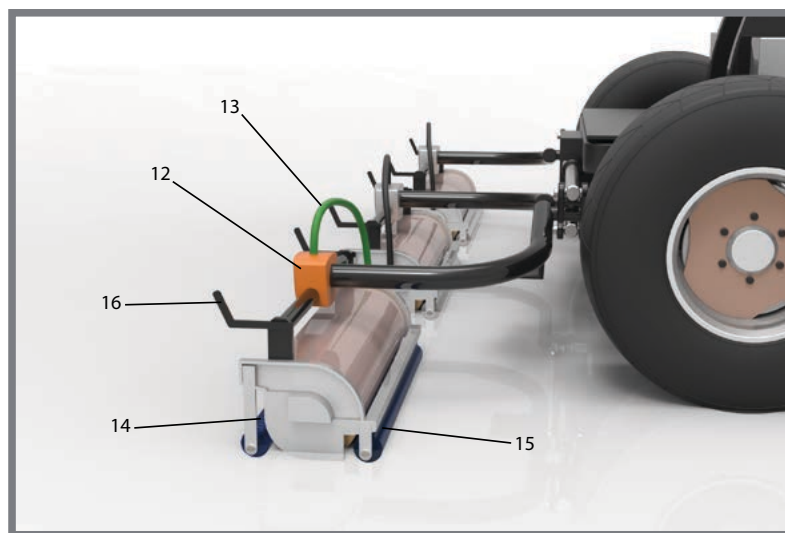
Finální technické řešení - detail předního mechanismu ramen
